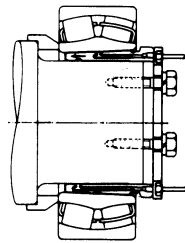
Instalação com Bucha Especial e Pressão Hidráulica
